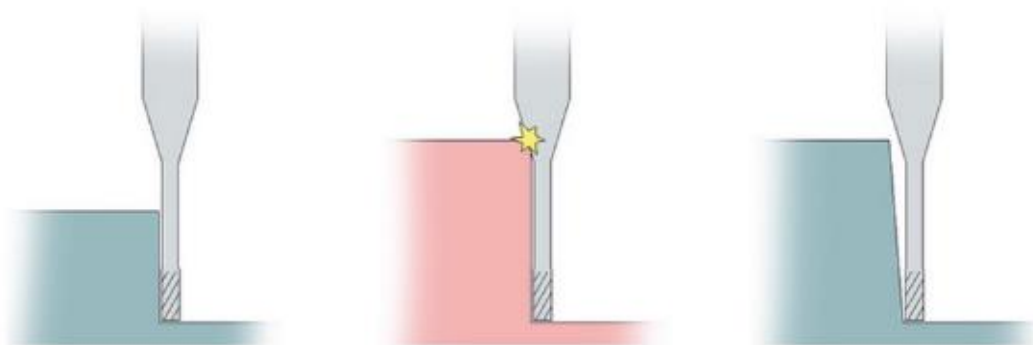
Limitações da fresadora de 3 eixo em usinagem de forma 3D
